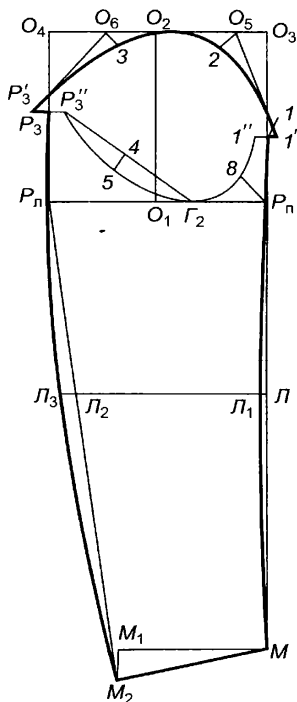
Креслення базисної сітки вшивного рукава
